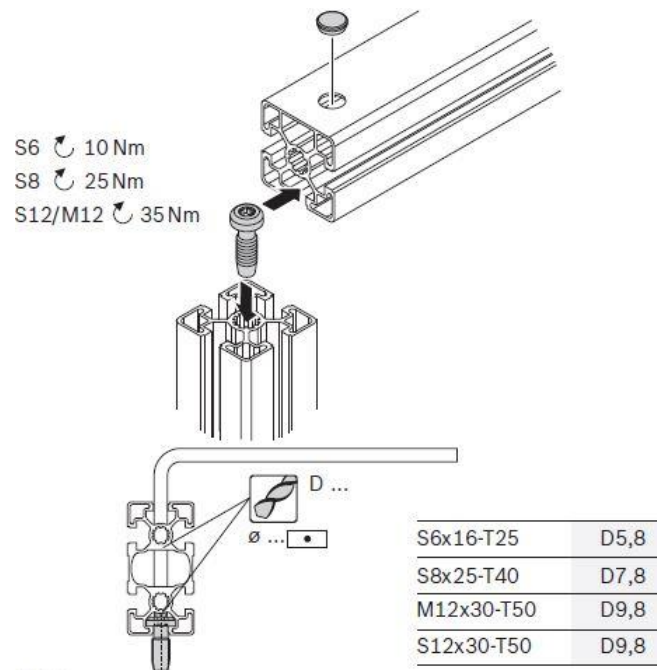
Názorné zobrazení šroubového spoje [29]
